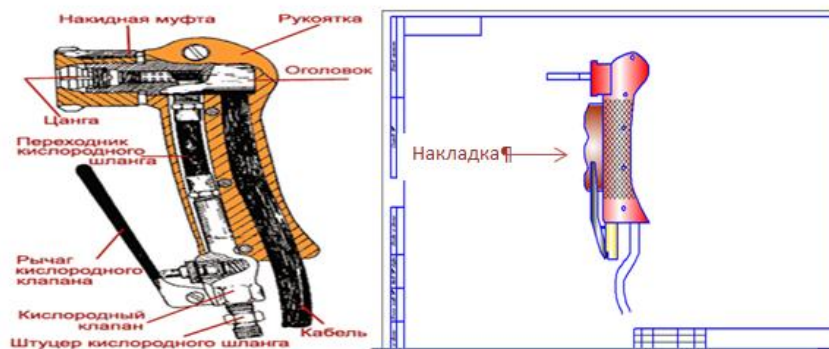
Стандартная рукоятка сварочного агрегата Рисунок 5. Изменение в конструкции рукоятки рычага кислородного клапана
